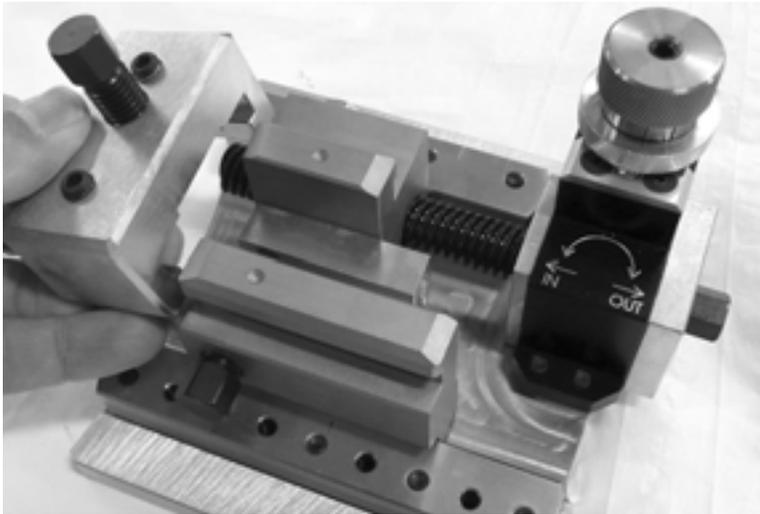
Das Foto zeigt die Komponenten des Innenbearbeitung-Werkzeugschlittens.
